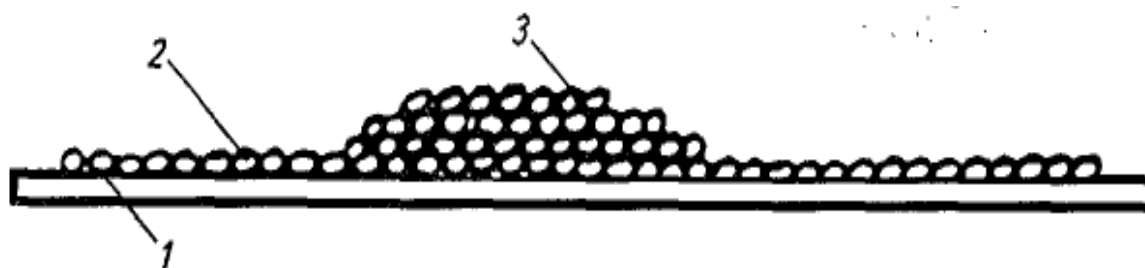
Схема розташування пастоподібного припою на поверхні стрічки:
